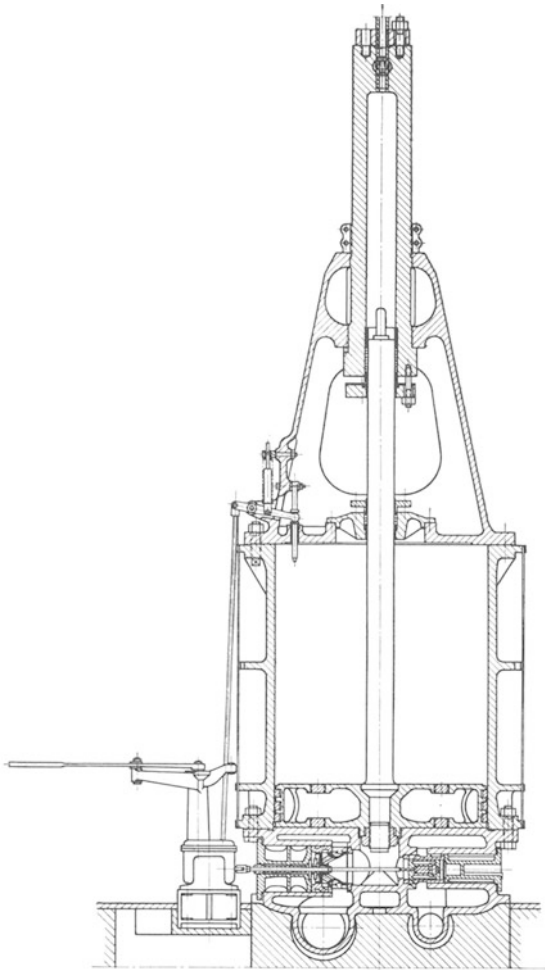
Lufttreibapparat mit oberem Druckwasserzylinder. Einbau der Steuerung im Zylinderboden. Antrieb des Abstellgestänges durch Anschlagen des Kolbens gegen einen Bolzen im Zylinderdeckel. (Kreuser G. m. b. H., Hamm i. W.)
